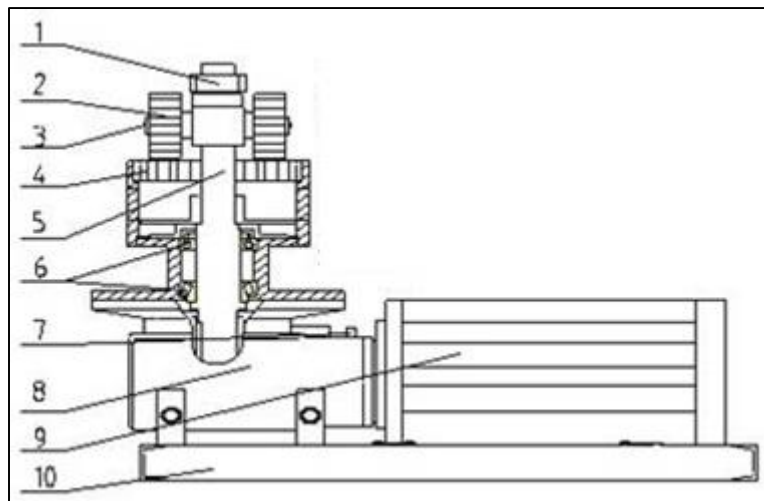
Componentes de la máquina pelletizadora. *Referencia:* 1) Tuerca de ajuste. 2) Rodillos. 3) Boquilla de lubricación de rodillos. 4) Matriz plana. 5) Eje principal. 6) Rodamientos. 7) Boquilla de lubricación de reductor. 8) Reductor. 9) Motor. 10) Base soporte.
